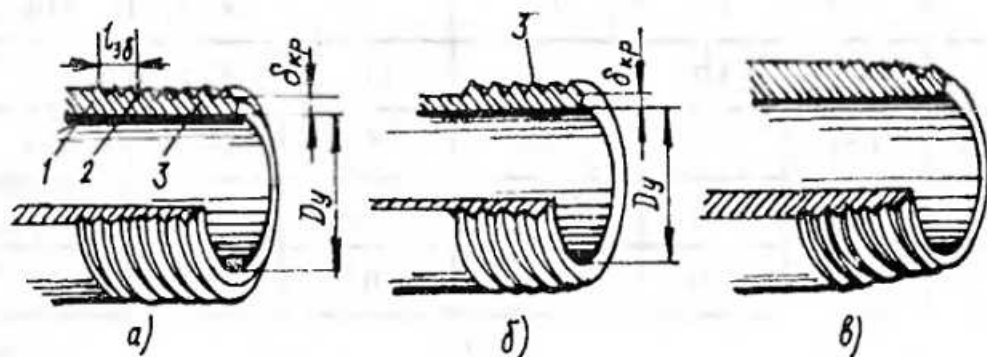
Трубні різі: а) циліндрична нарізана; б) циліндрична накочена; в) конічна; 1 - труба; 2 - збіг; 3 - робоча частина
